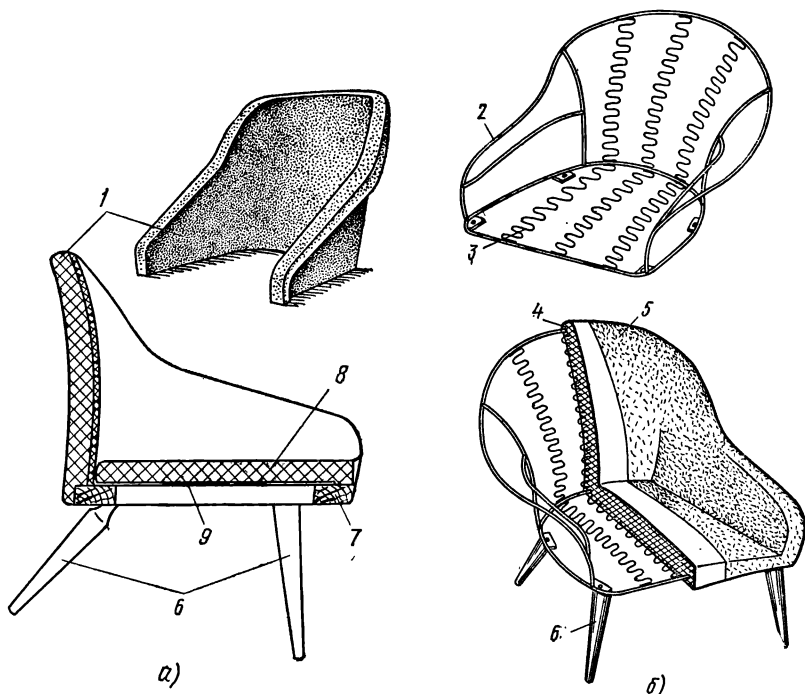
Конструкция кресел с блоками, отлитыми из жесткого (а) и эластичного (б) пеноматериала:
